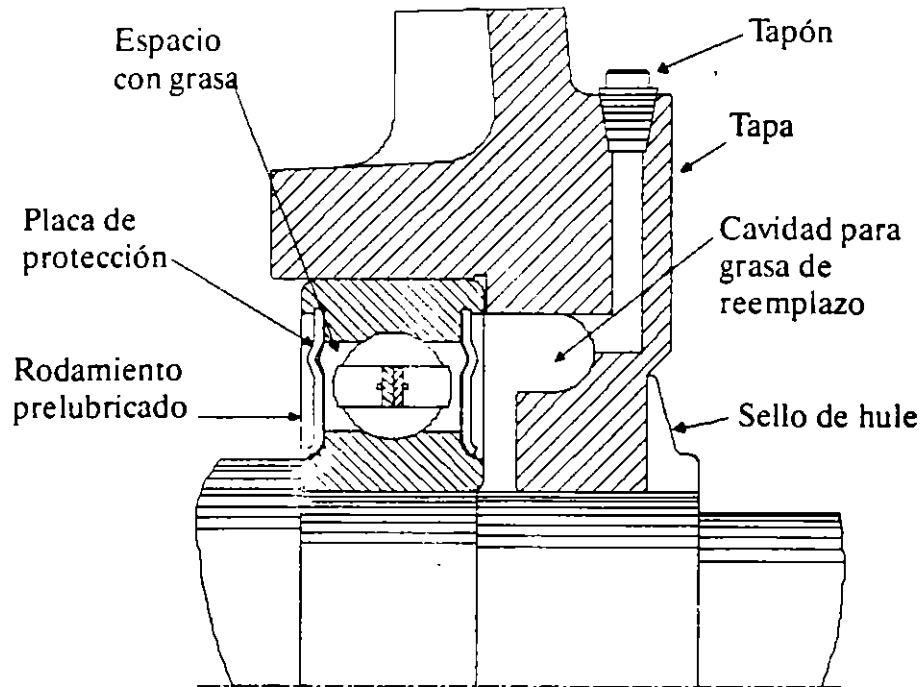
Vista en sección de un rodamiento prelubricado, tapa y flecha.
